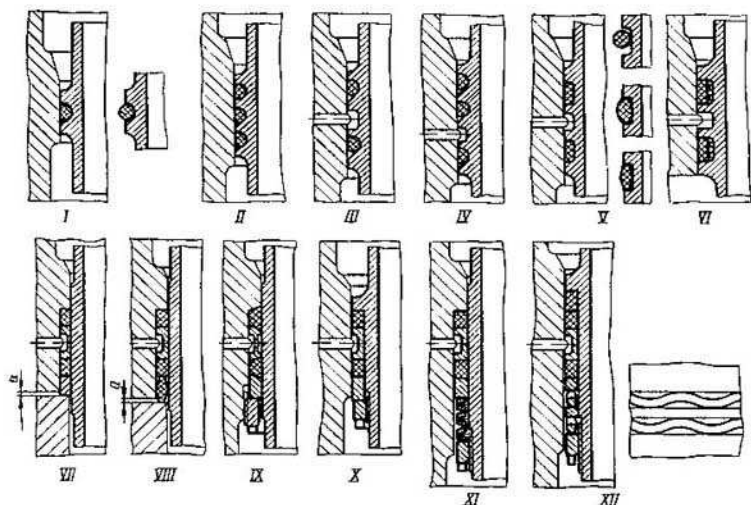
Estancamiento de juntas cilíndricas para líquidos
